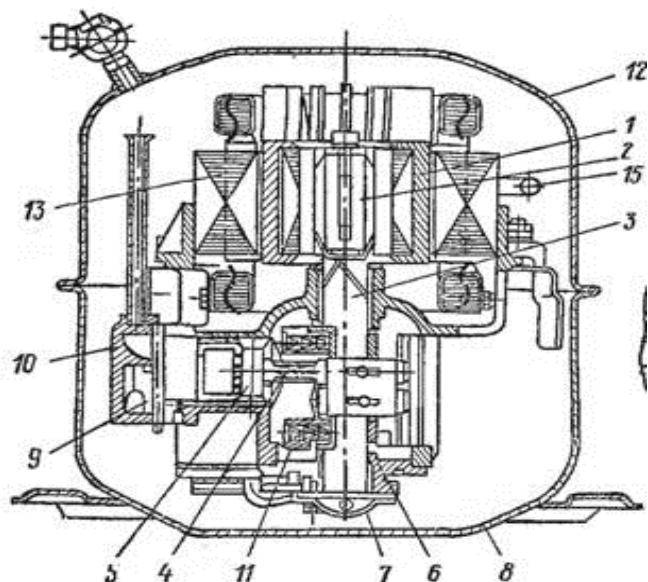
Герметичный компрессор ФГ-0,7~3
